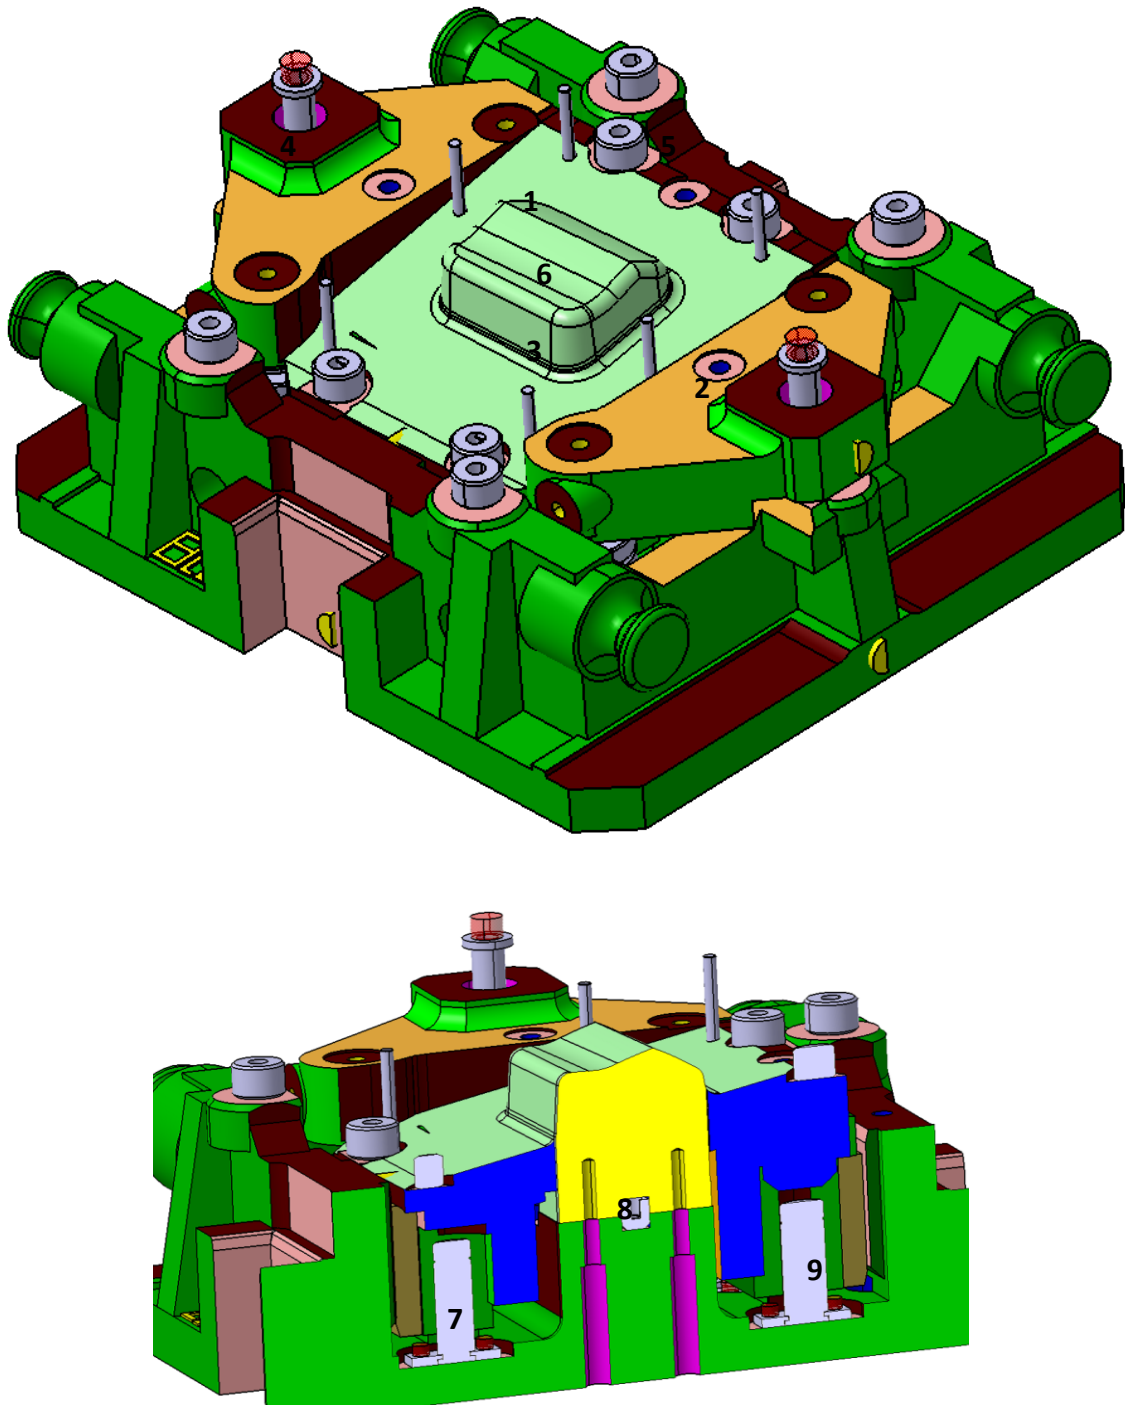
spodní část tažníku je opatřena drážky pro pero
